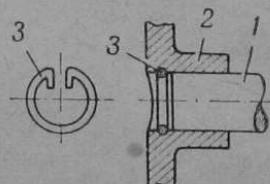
Крепление поршневого пальца на двигателе M-72:
